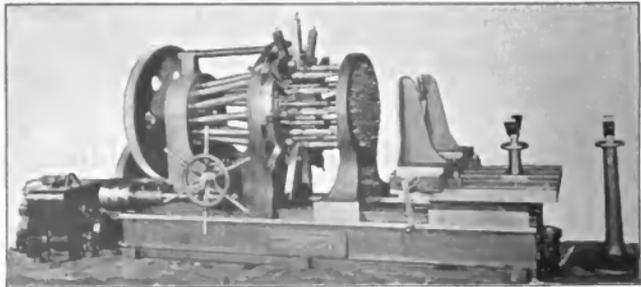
Mehrspindlige Patent-Phönix-Bohrmaschine.
